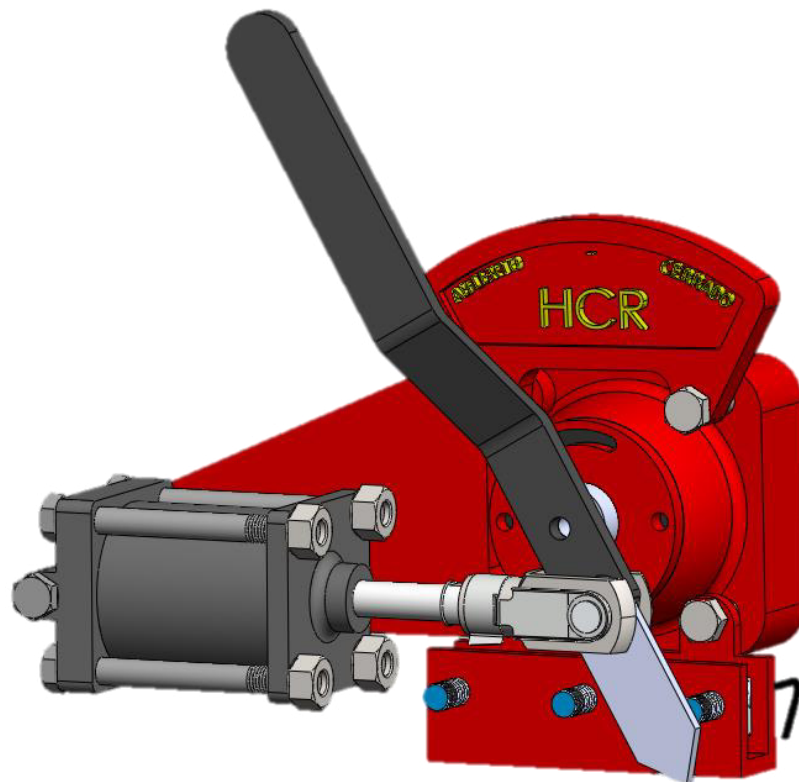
Diseño CAD, ensamble de soporte de sensores.
